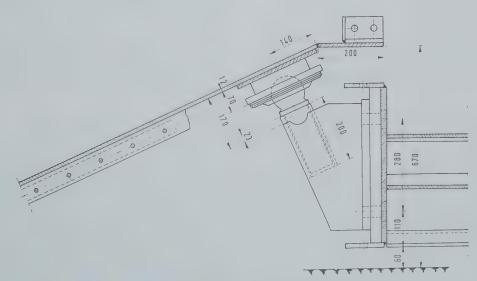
Assemblage par rotule entre estacade et châssis de tête motrice.
